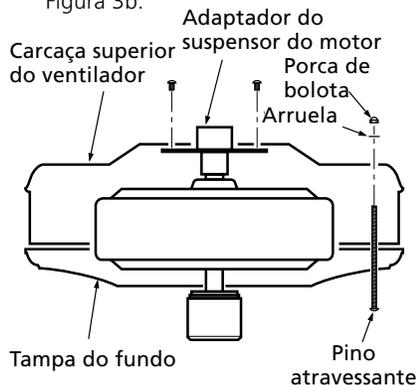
Montando e fixando as carcaças ao adaptador do suspensor do motor
